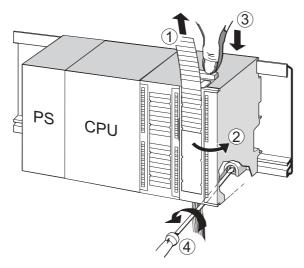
Frontstecker entriegeln und Baugruppe demontieren
